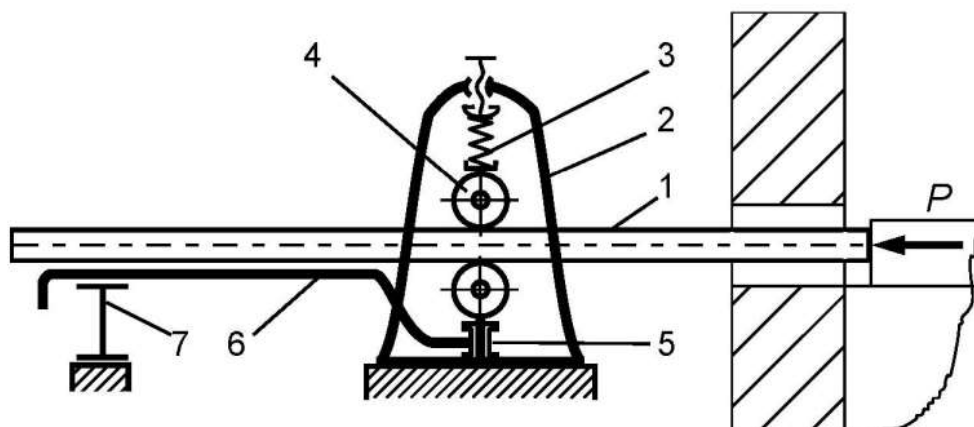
Схема фрикционного выталкивателя: 1 - штанга;
